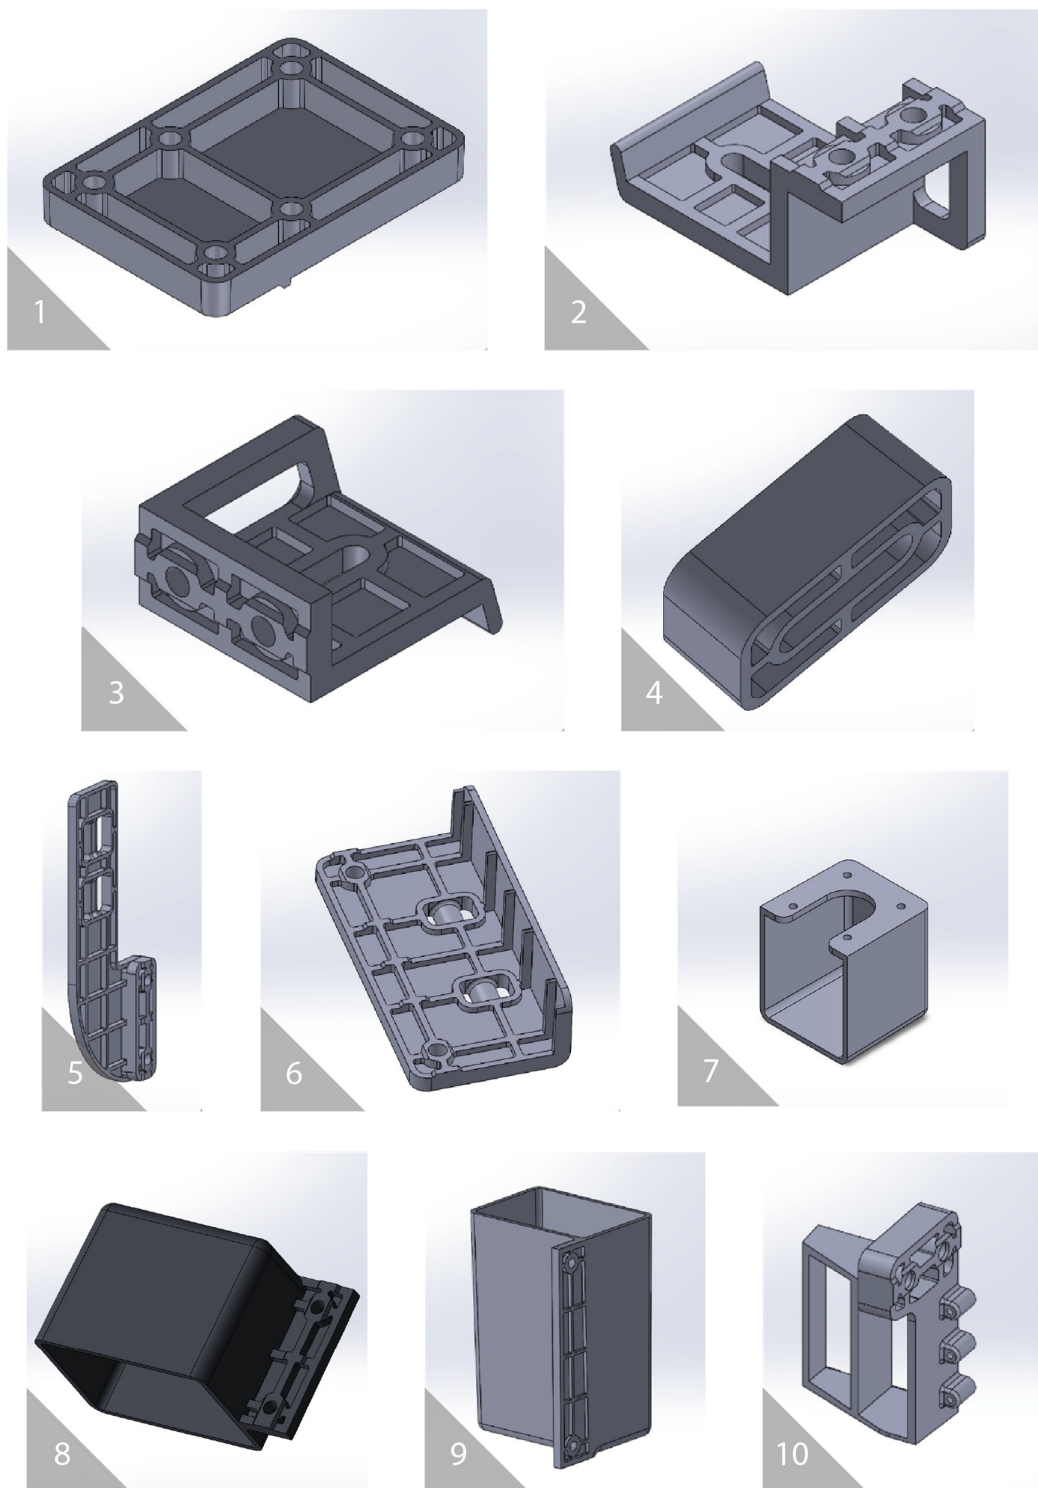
Piezas plásticas del modelo inicial Farmbot Express V1.0. De izquierda a derecha y de arriba a abajo 1. Gantry Plate Spacer Block, 2. 40mm Horizontal Cable Carrier Support, 3. 40mm Vertical Cable Carrier Support, 4. 40mm Cable Carrier Spacer Block, 5. Solenoid Valve Mount, 6. Vacuum Pump Mount, 7. 50mm Horizontal Motor Housing, 8. 60mm Vertical Motor Housing, 9. Vacuum Pump Cover, 10. Seed Though Holder [25].
